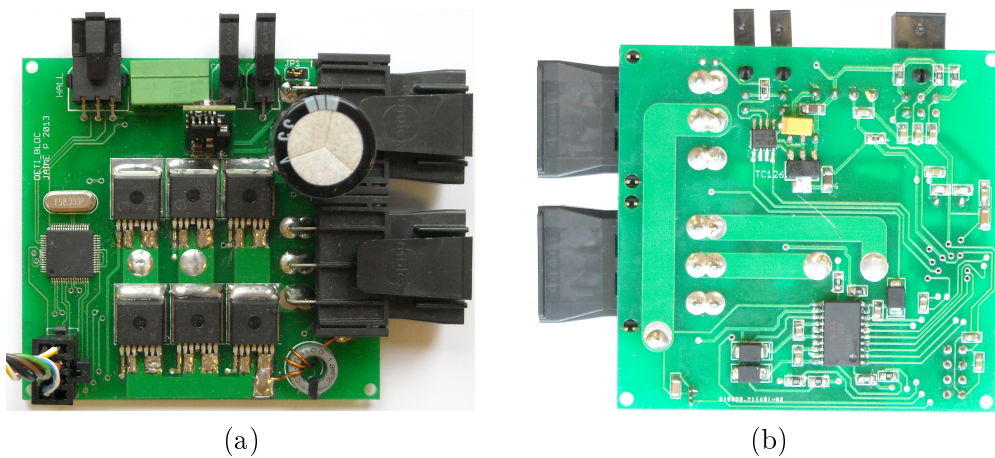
(a) PCB Final - Top (b) PCB Final - Bottom
